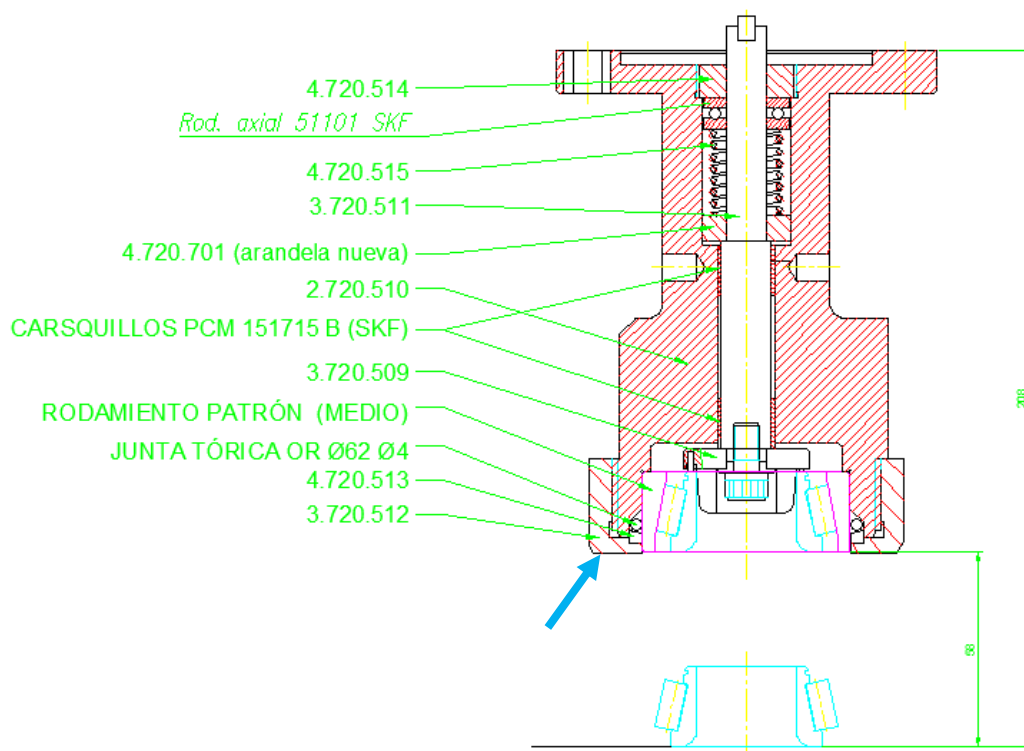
Vista seccionada de las piezas afectadas al error.
